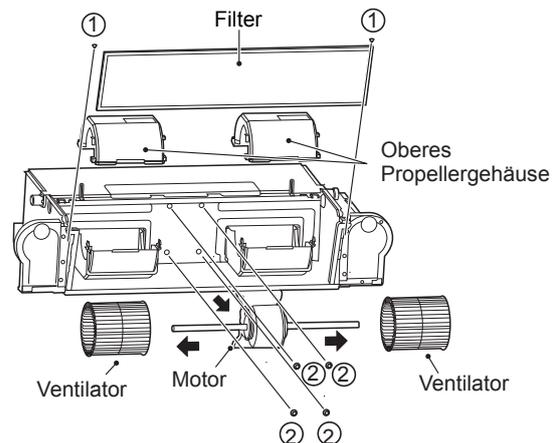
Demontage der Luftfilter-, Deckel- und Motorschrauben
